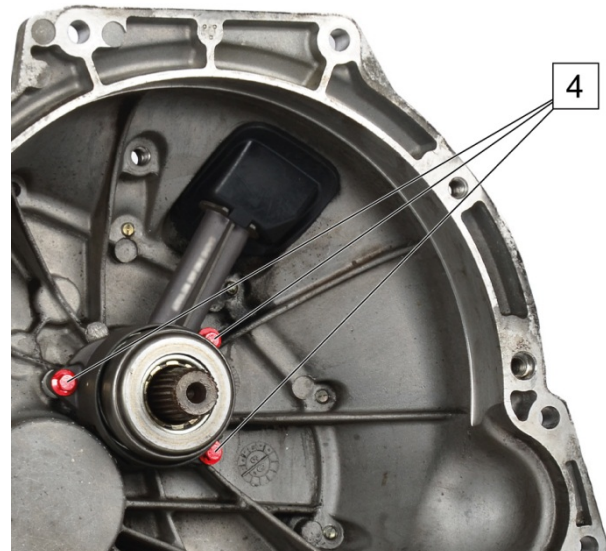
CSC montiert / CSC assembled / Butée hydraulique montée / CSC montado
